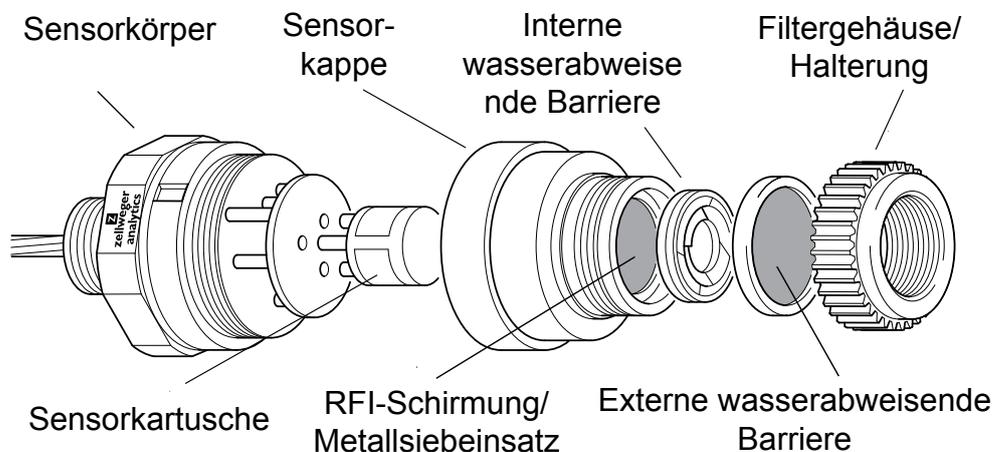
Explosionszeichnung des Sensepoint Sensors für toxische Gase
